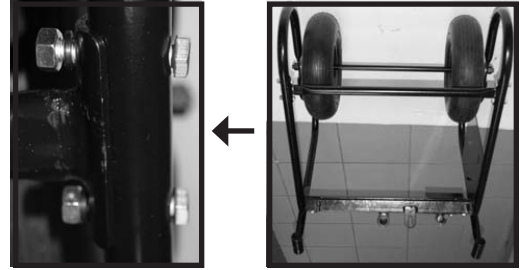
Pièces requises pour l'assemblage du cadre.
